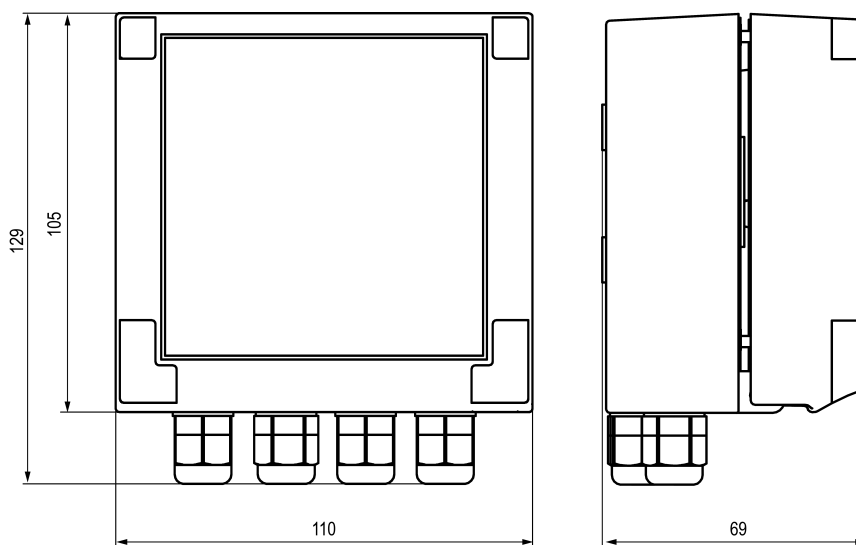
Габаритные размеры прибора в корпусе Н
